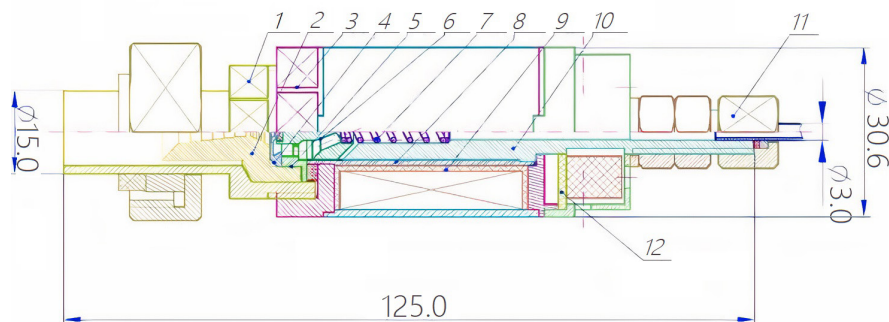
Схема газового клапана для испытаний прототипов седла и сопла:
